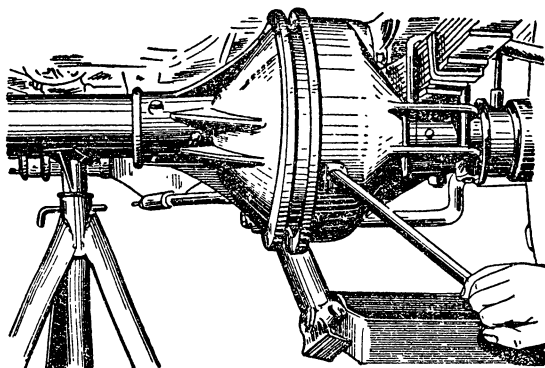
Разъединение картера переднего моста и вывод из зацепления ведомой шестерни с ведущей
